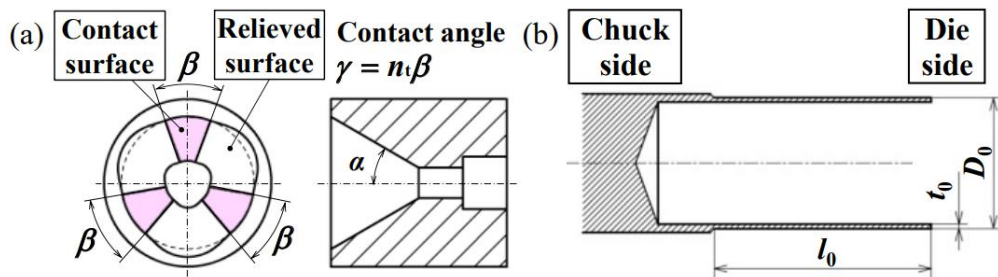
Конструктивні параметри а) матриці та б) заготовки [28]
